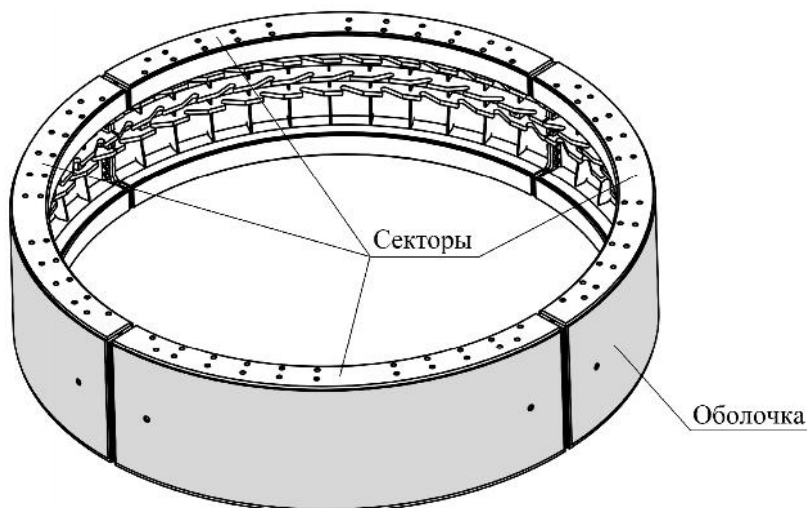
Общий вид внешнего корпуса модуля сопряжения геохода
